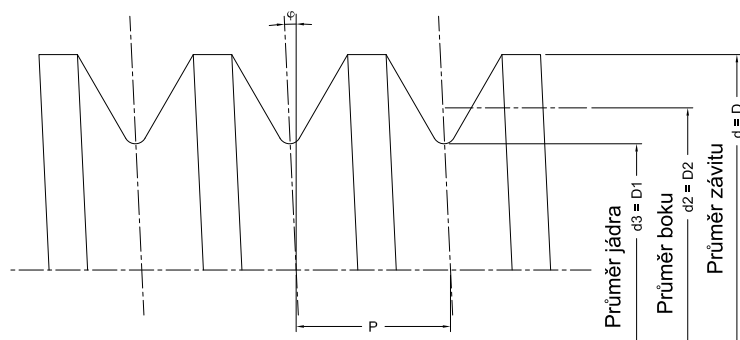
Pravý závit se šroubem soustruhu otáčejícím se doprava
